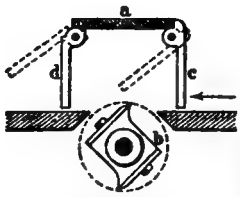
Schutzvorrichtung an Hobelmaschinen.
